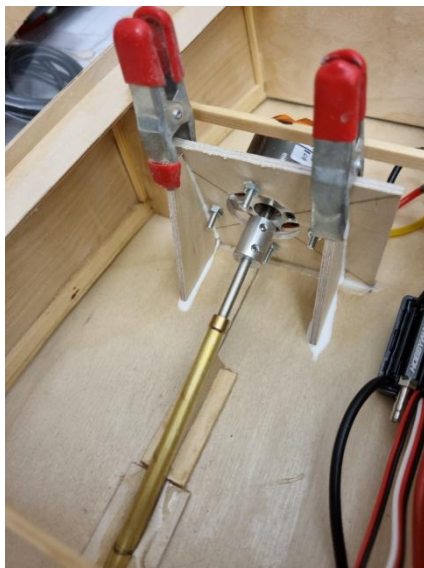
Fixierung des Stevenrohrs unter dem Rumpfboden beim Einkleben
